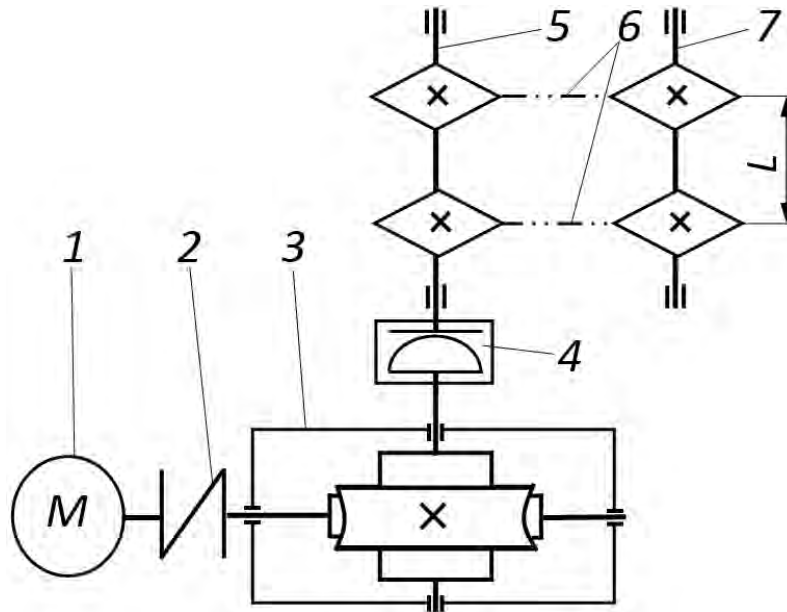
Схема привода цепного конвейера (вид сверху): 1 – асинхронный электродвигатель; 2 – муфта упругая втулочно-пальцевая; 3 – редуктор червячный с нижним расположением червяка; 4 – муфта кулачково-дисковая; 5 – промежуточный вал; 6 – цепные передачи с разделенным потоком мощности; 7 – приводной вал с двумя приводными звездочками и шлицевыми отверстиями на торцах
